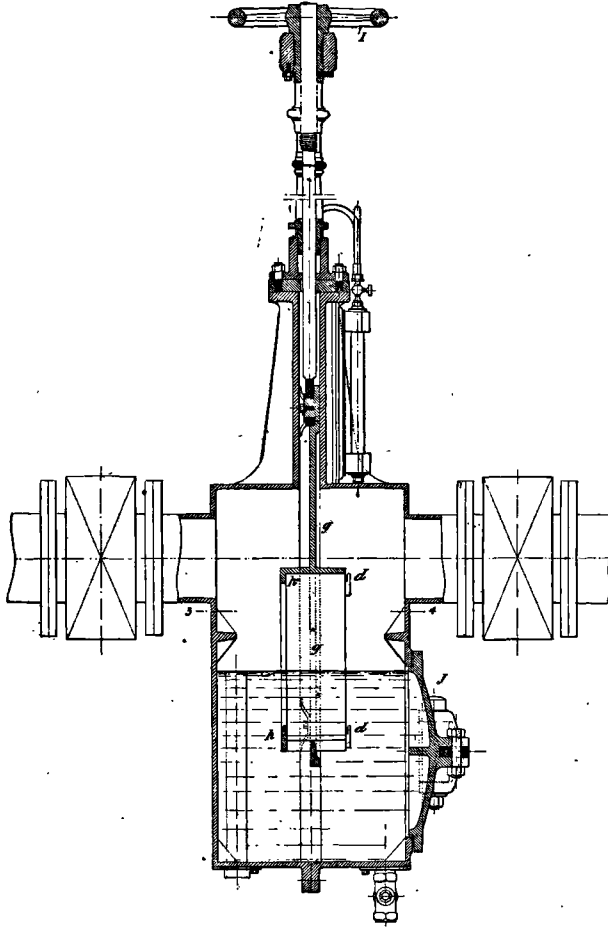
Épurateur Lencauchez. — Coupe et vue d'ensemble.
